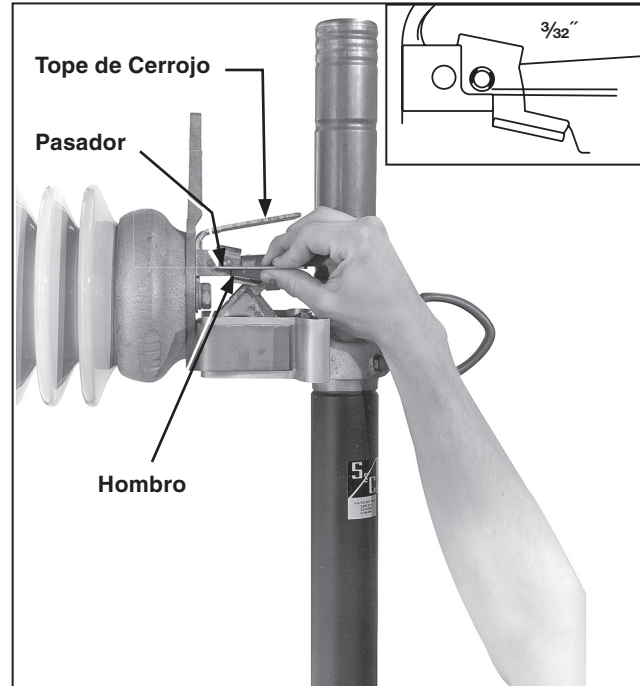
Revisión de la separación entre el pasador del conjunto de enganche y la pieza fundida de contacto del hombro.
